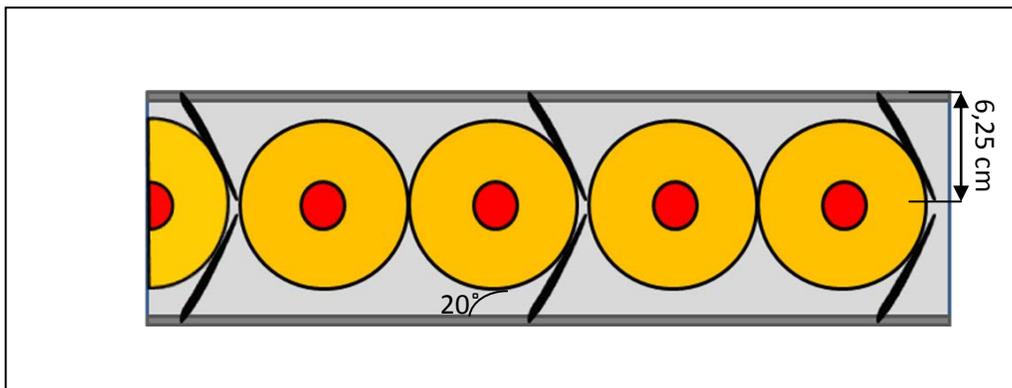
Vista de planta de la banda con el sistema de frenos-guías
